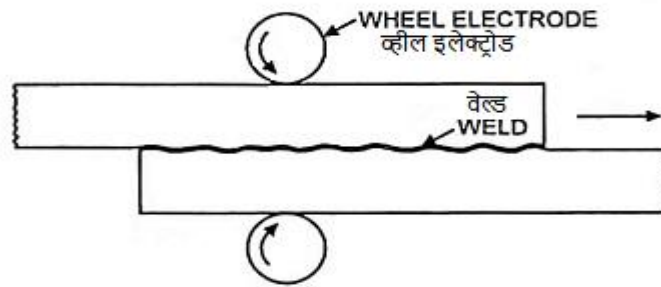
सीम वेल्डिंग (Seam Welding)
